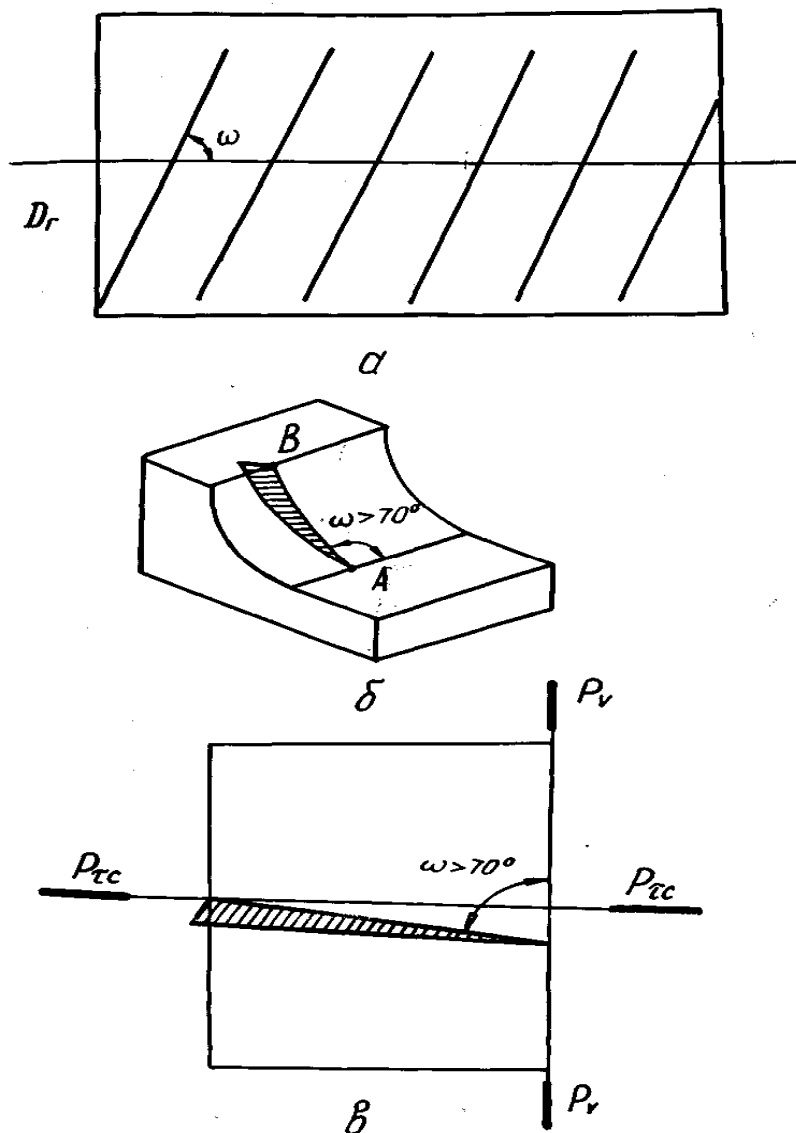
Схема скользящего цилиндрического фрезерования
